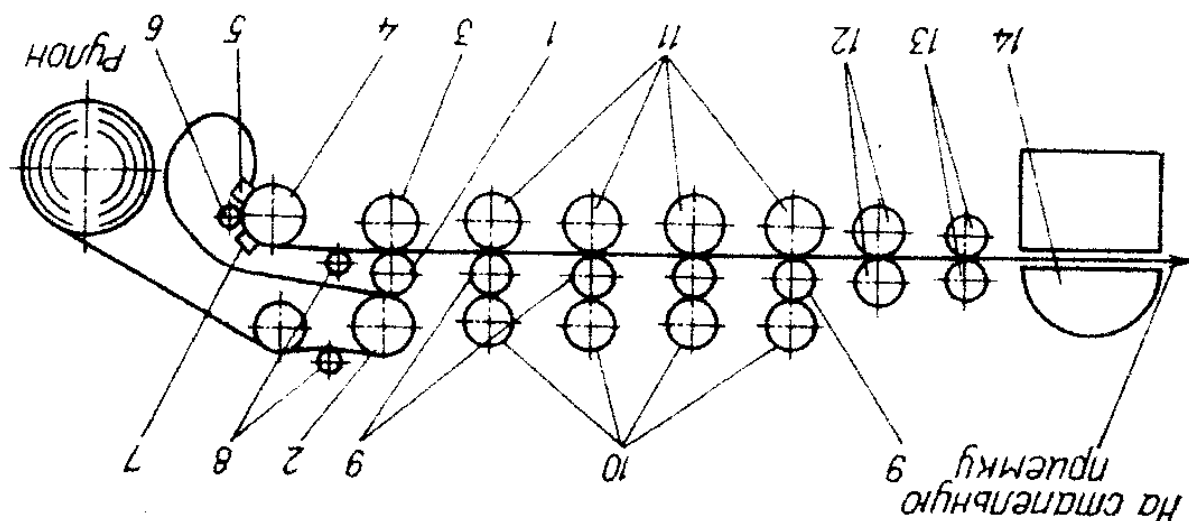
Картонопроводящая схема печатно-высекательного автомата марки СДА-111: 1 – форматный валик; 2,3 – прижимные цилиндры; 4 – направляющий цилиндр; 5 – войлочный тормоз; 6 – щетка; 7 – направляющий упор; 8 – правильные валики; 9 – обрезиненные офсетные валики; 10 – клишейные валики; 11 – печатные цилиндры; 12 – промежуточный механизм натяжения; 13 – валики периодической подачи; 14 – штанцевальный аппарат
